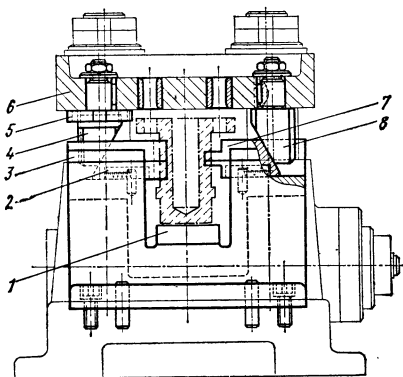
Наладка скалчатого кондуктора для сверления двух отверстий во фланце втулки
